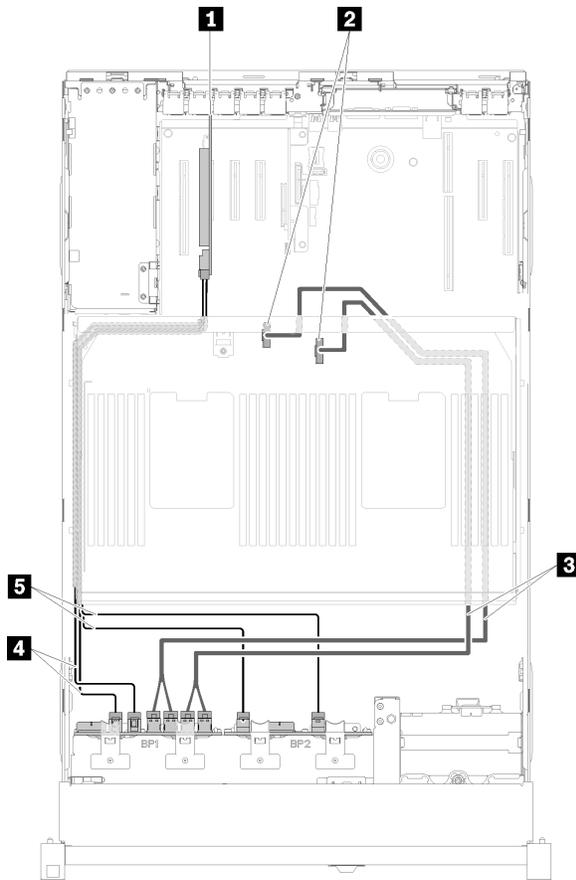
Instradamento dei cavi, Backplane AnyBay + Backplane a 8 vani
